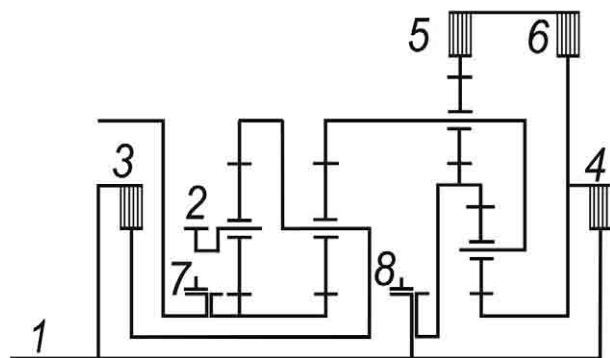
Кинематическая схема ГМП ZF9HP: 1 — входной вал; 2 — выходное зубчатое колесо; 3, 4 — фрикционная муфта; 5, 6 — фрикционный тормоз; 7, 8 — зубчатая муфта
